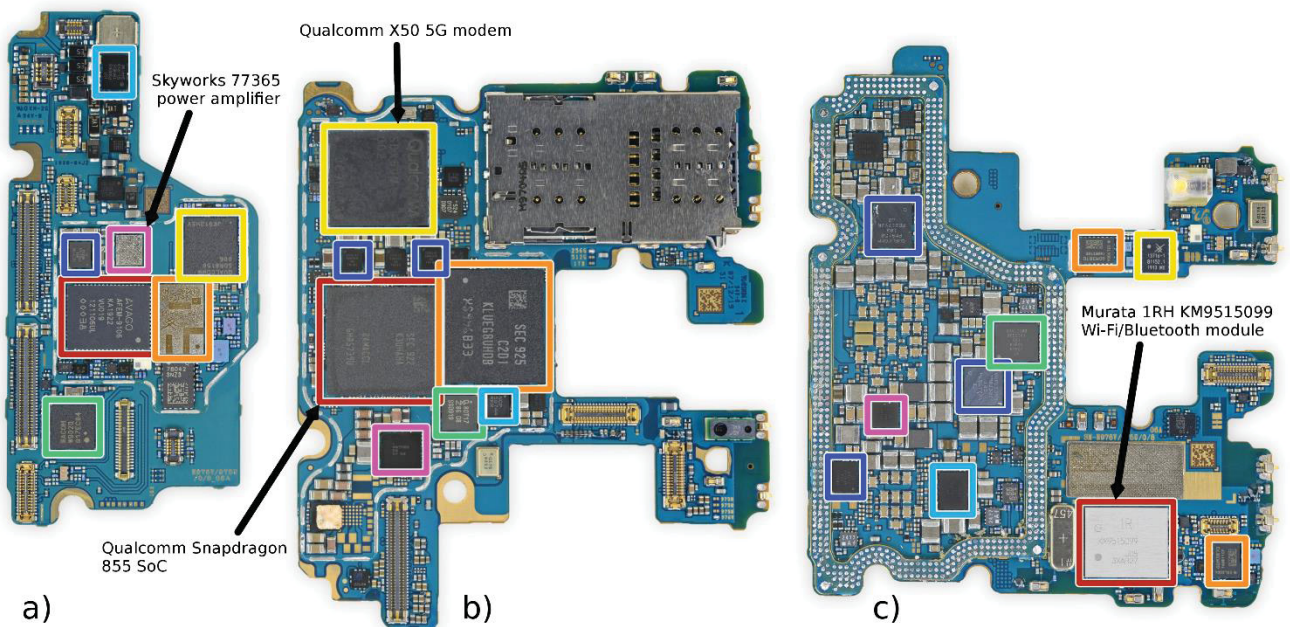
Detalhe de (a) placa PCB auxiliar, visão (b) frente e (c) verso da placa principal, com indicação dos componentes de RF de interesse (Ifixit, 2019).
